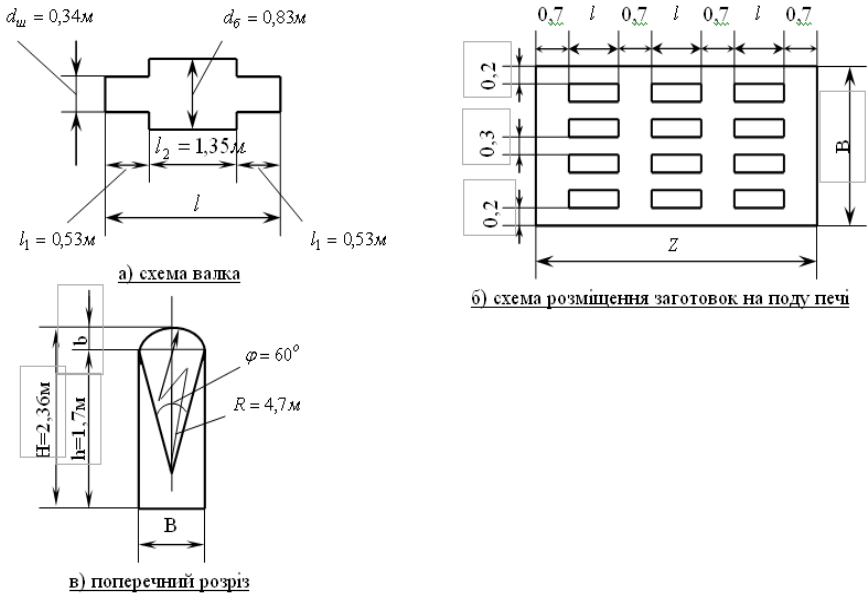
Схема валка, розміщення заготовок на поду печі та поперечний розріз робочого простору.
